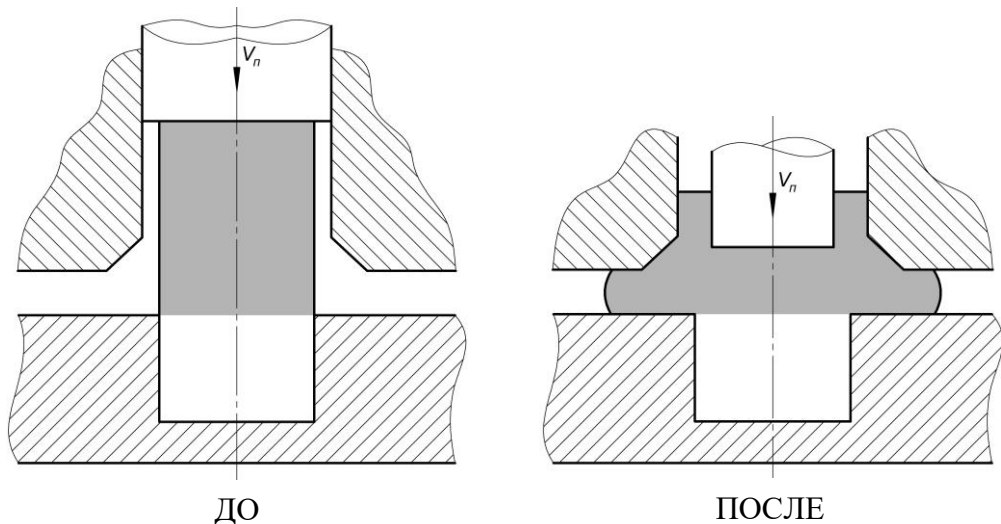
Формирование цилиндрической заготовки в процессе комбинированного выдавливания
